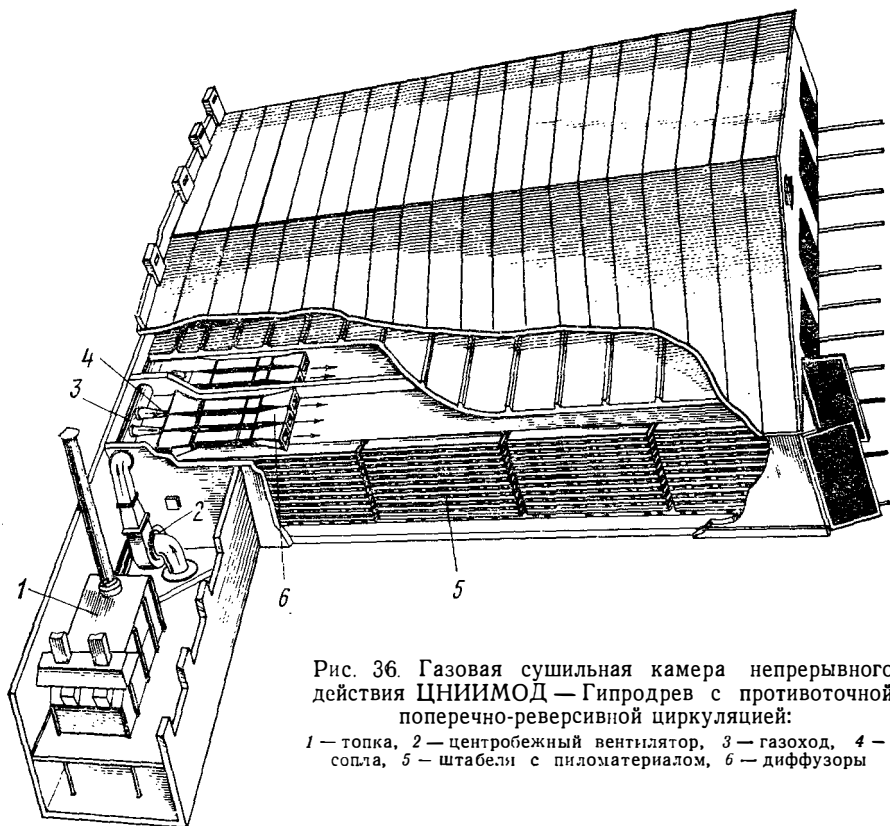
Газовая сушильная камера непрерывного действия ЦНИИМОД — Гипродрев с противоточной поперечно-реверсивной циркуляцией:
